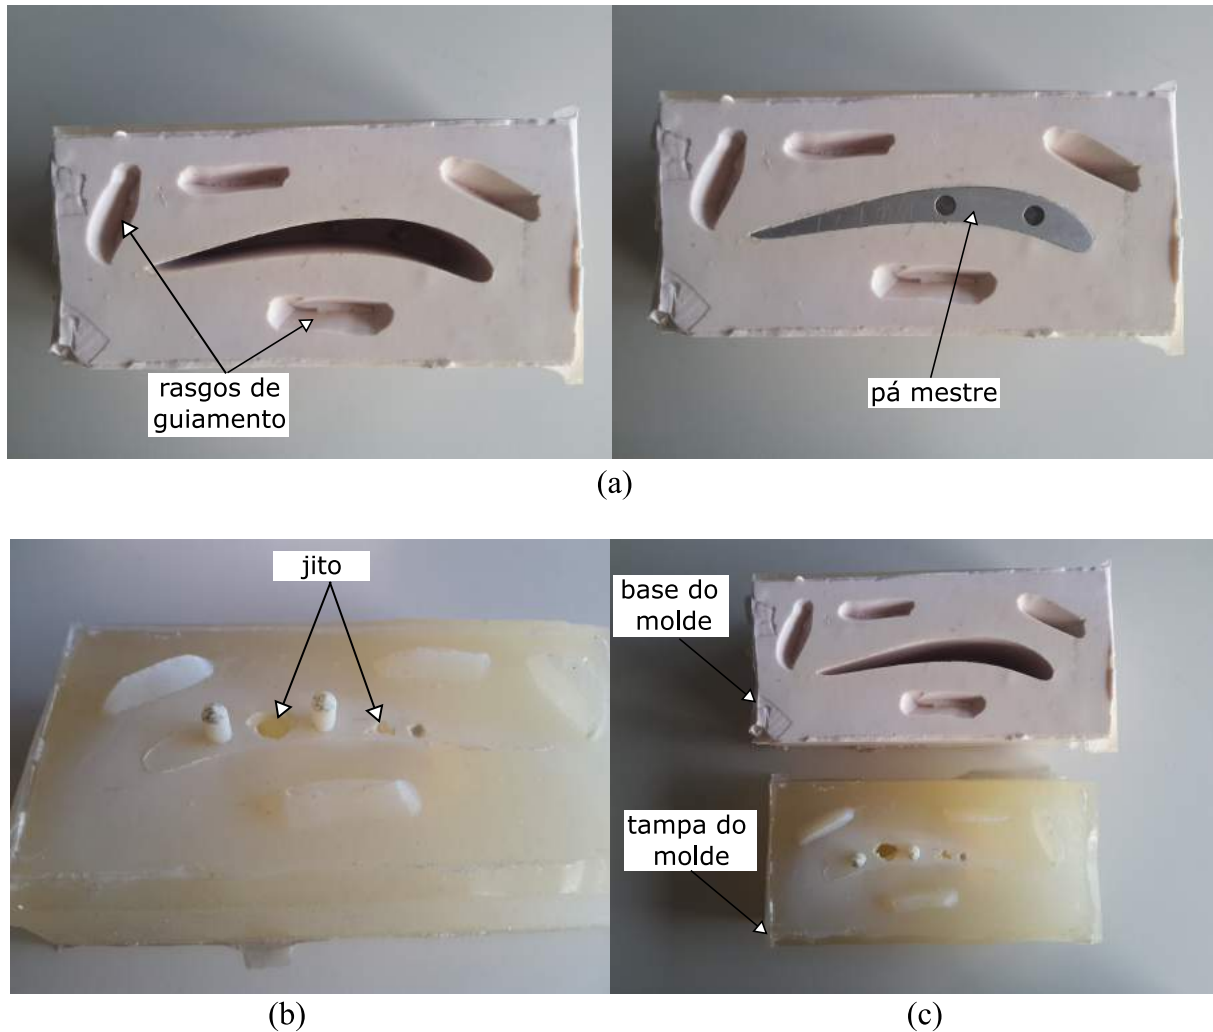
Moldes de silicone: (a) base do molde com e sem a pá mestre; (b) tampa do molde; (c) conjunto tampa e base do molde.
